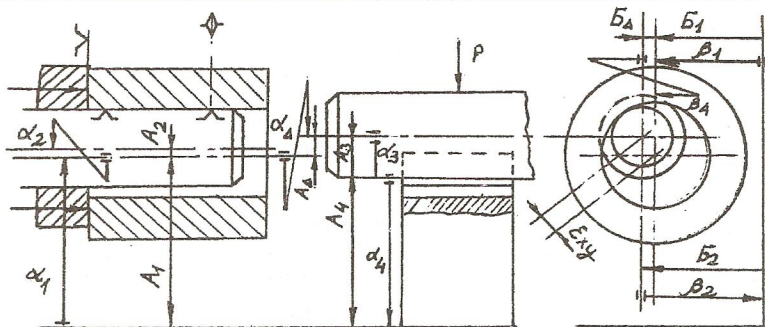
Базирование собираемых деталей на цилиндрическую и призматическую поверхности
